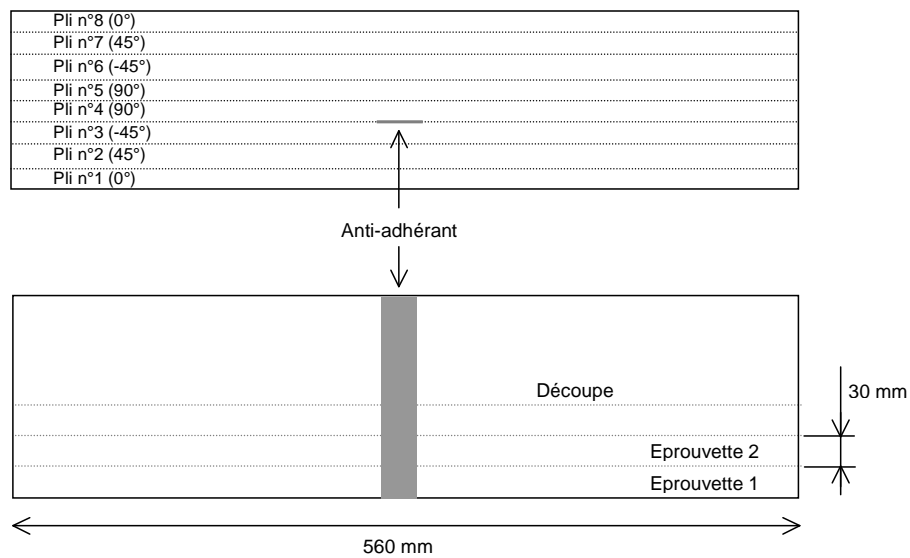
Création du délaminage et découpe des éprouvettes.
